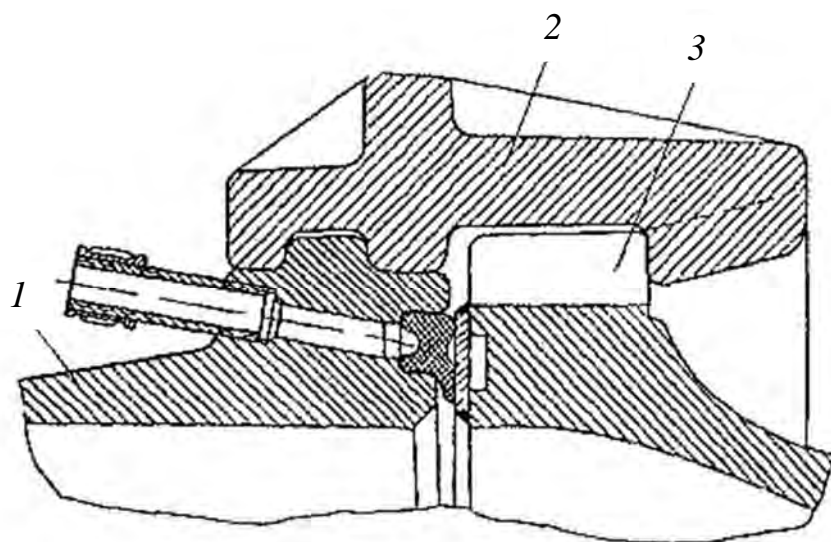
Поворотное байонетное кольцо крышки: 1 – корпус автоклава; 2 – байонетное кольцо; 3 – зуб крышки
